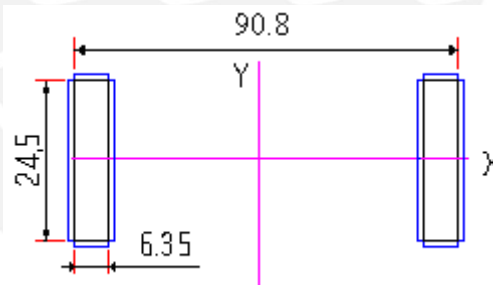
Esquema para cálculo de la inercia de cordones de soldadura de los pies de la torre fija 2.
